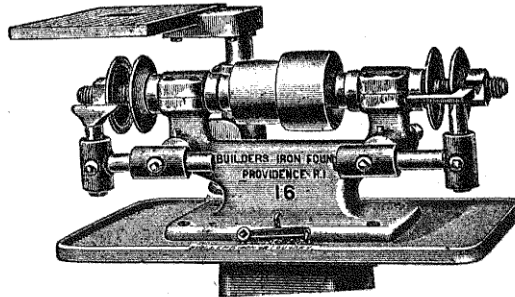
Machine Builders avec dispositif pour meuler des surfaces planes.
